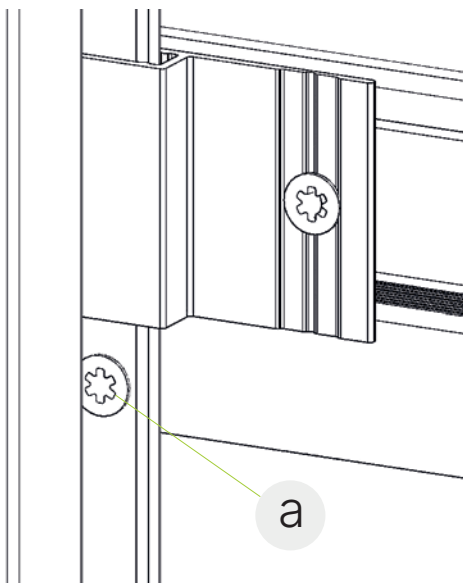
Fijación del perfil de fachada con tornillo autorroscante.
